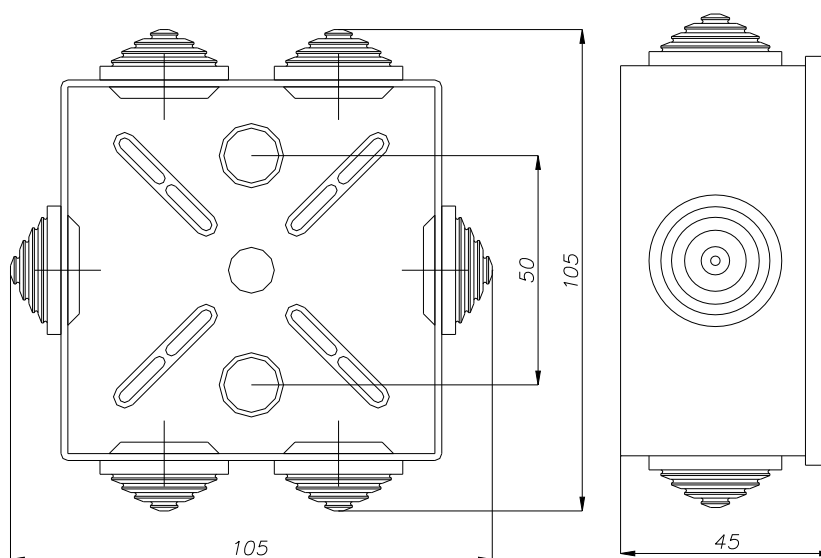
Габаритные и установочные размеры разветвителя КРИ-6.
